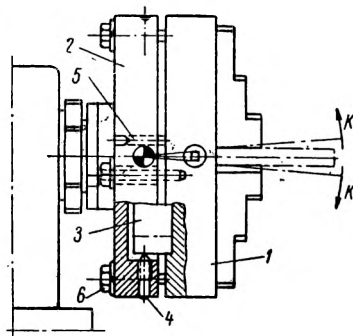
Трехкулачковый патрон с устройством для выверки.
